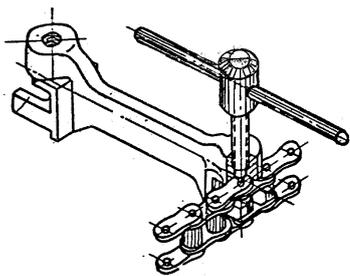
Приспособление для разборки втулочно-роликовых цепей
